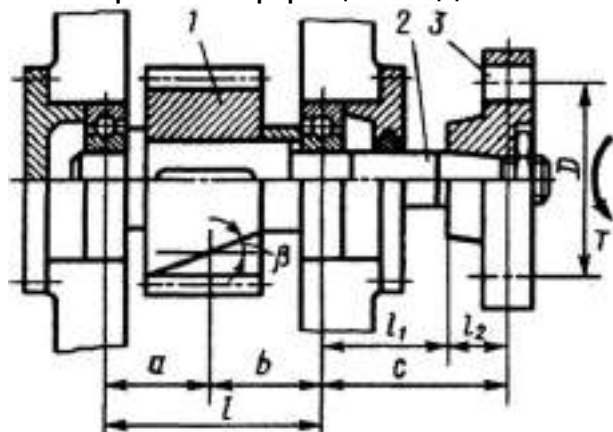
Вал с элементами, расположенными на нем: 1 – шестерня; 2 – вал; 3 – полумуфта
